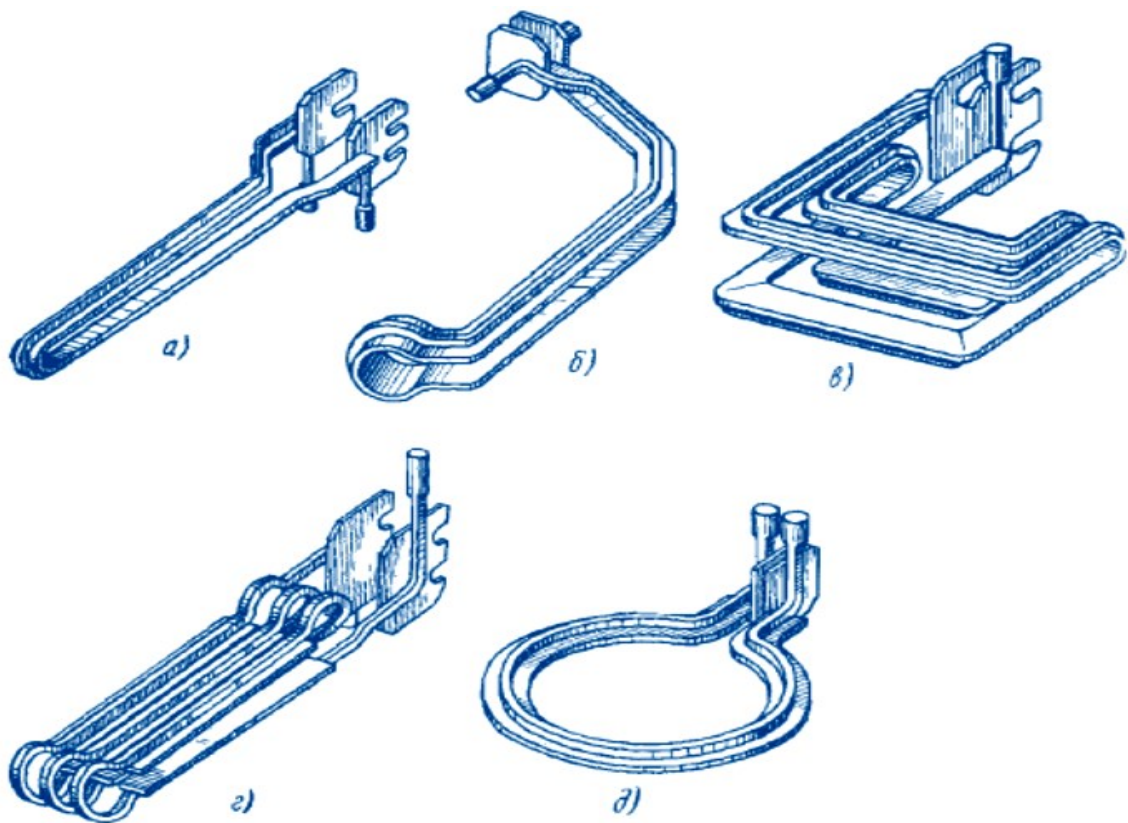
Індуктори для наплавлення тонких плоских деталей машин [51, 2]:
